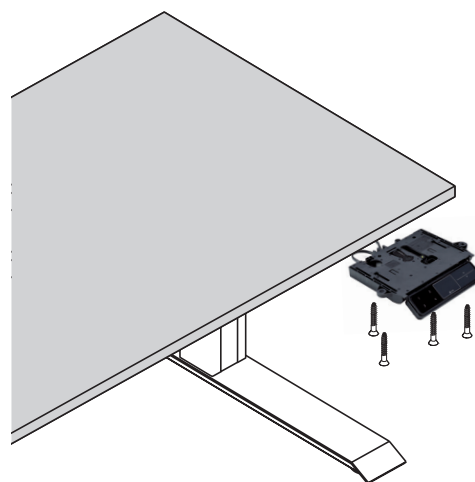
Handschalter LegaDrive Touch Comfort anbringen
